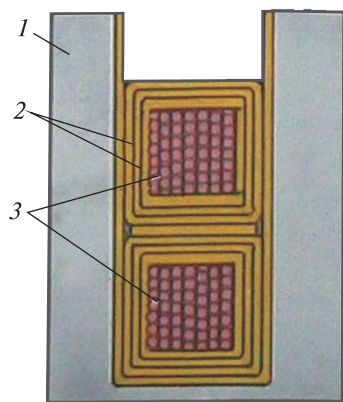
Паз и обмотка якоря: 1 — сердечник якоря; 2 — изоляция; 3 — катушка якоря
